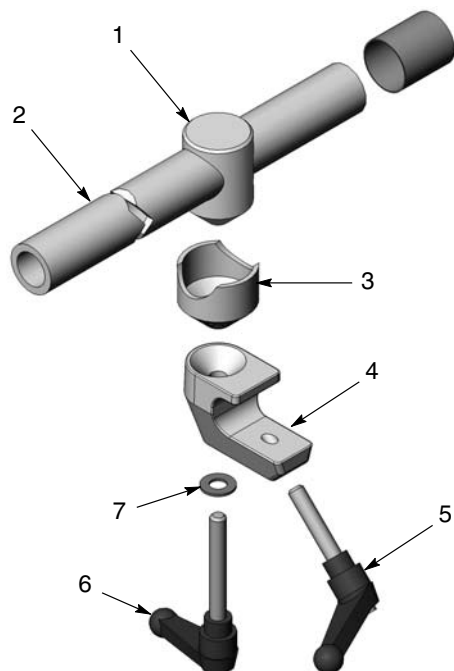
Uchwyt do pistoletów mocowanych na rurze w rowku T
